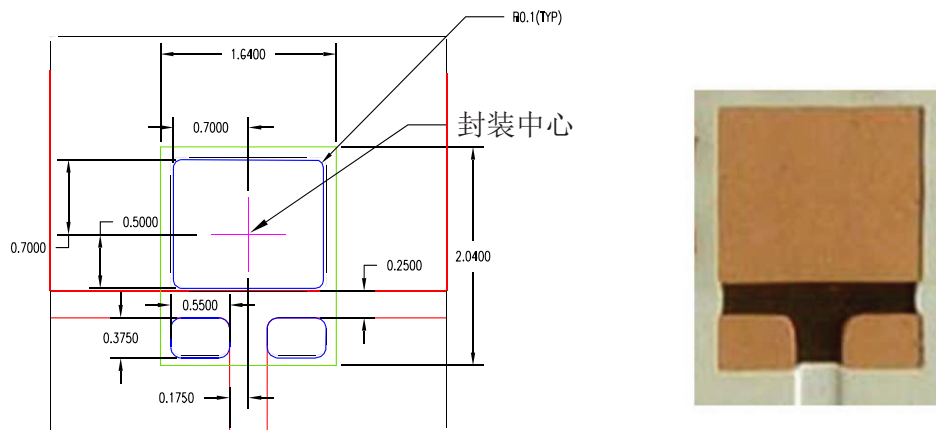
左图是被推荐的LUXEON PCB封装设计，右图是LUXEON PCB绿油开窗（无焊料）；所有尺寸以毫米（mm）计算。
